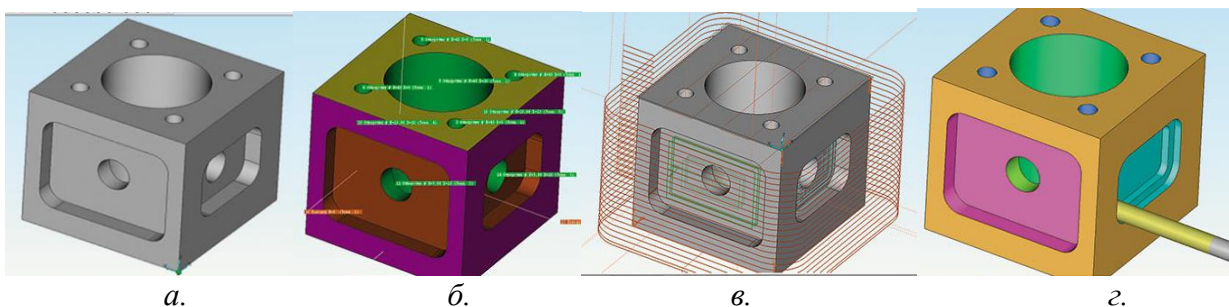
Приклад багатопозиційної фрезерної обробки: а. – найпростіша модель деталі, б. – зони обробки, в. – траєкторія руху, г. – симуляція процесу механообробки
